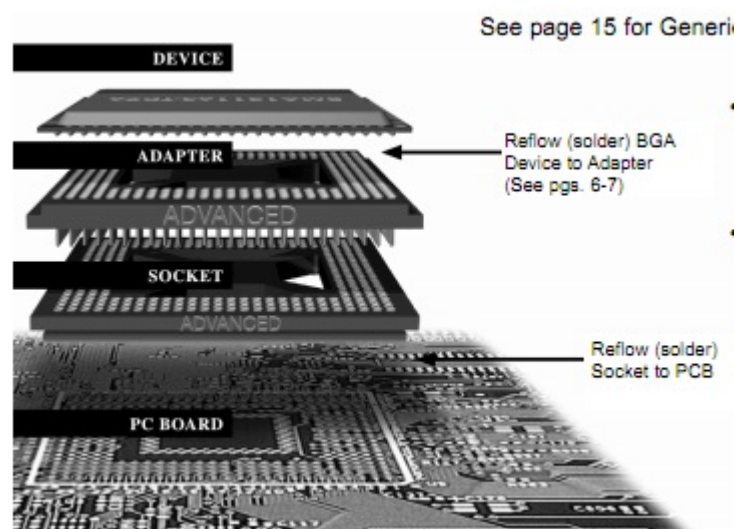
Vista de um PCB com aplicação do socket para BGA[ERMEC].
